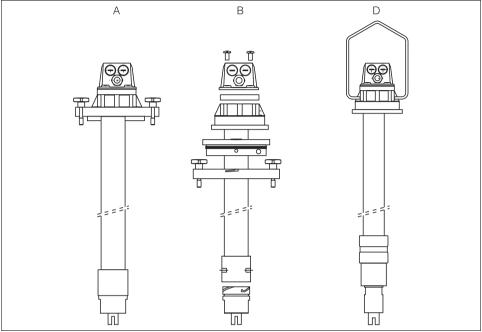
Dipfit CLA111, versiones de montaje A, B y D
